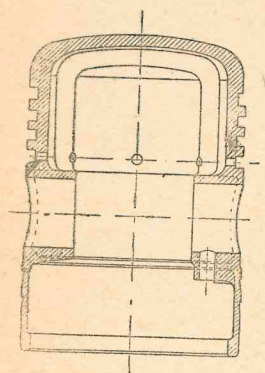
Поршень двигателя СТЗ—ХТЗ для генераторного газа
